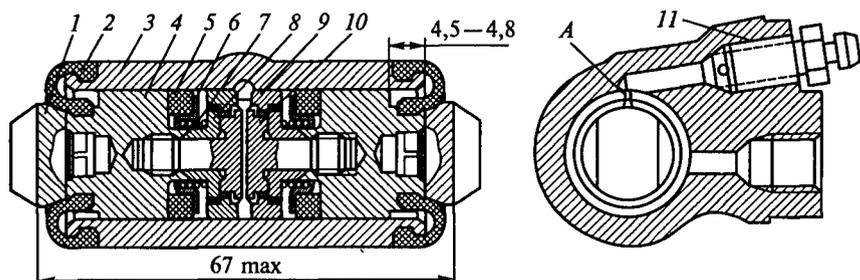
Колесный цилиндр с автоматическим устройством регулирования зазора между колодками и барабаном:
